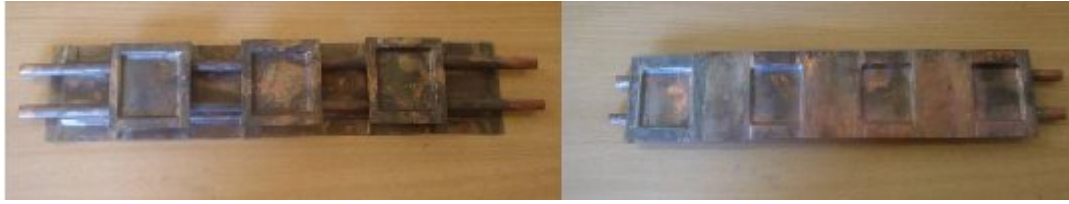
élément de l'échangeur après soudage.
